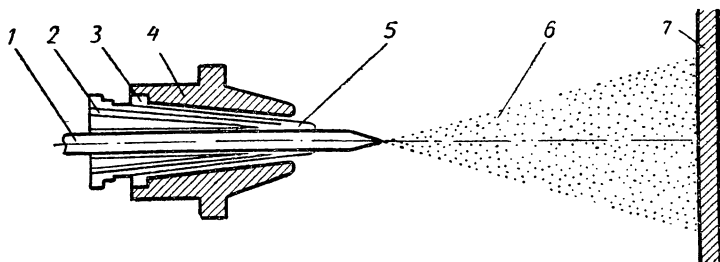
Напыление стержневым методом: 1 — спрессованный керамический стержень; 2 — канал подачи кислородно-ацетиленовой смеси; 3 — канал подачи сжатого воздуха; 4 — корпус форсунки; 5 — кислородно-ацетиленовое пламя; 6 — конус распыления наполненного материала; 7 — обрабатываемая деталь.
